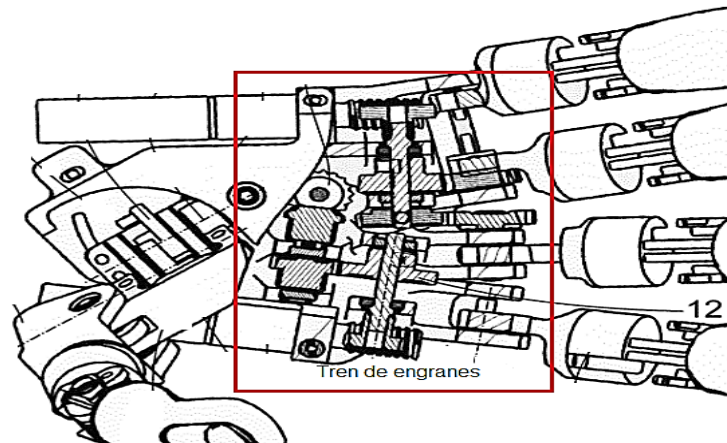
Conjunto de engranes para mover el movimiento de flexión y extensión para las falanges [23].
